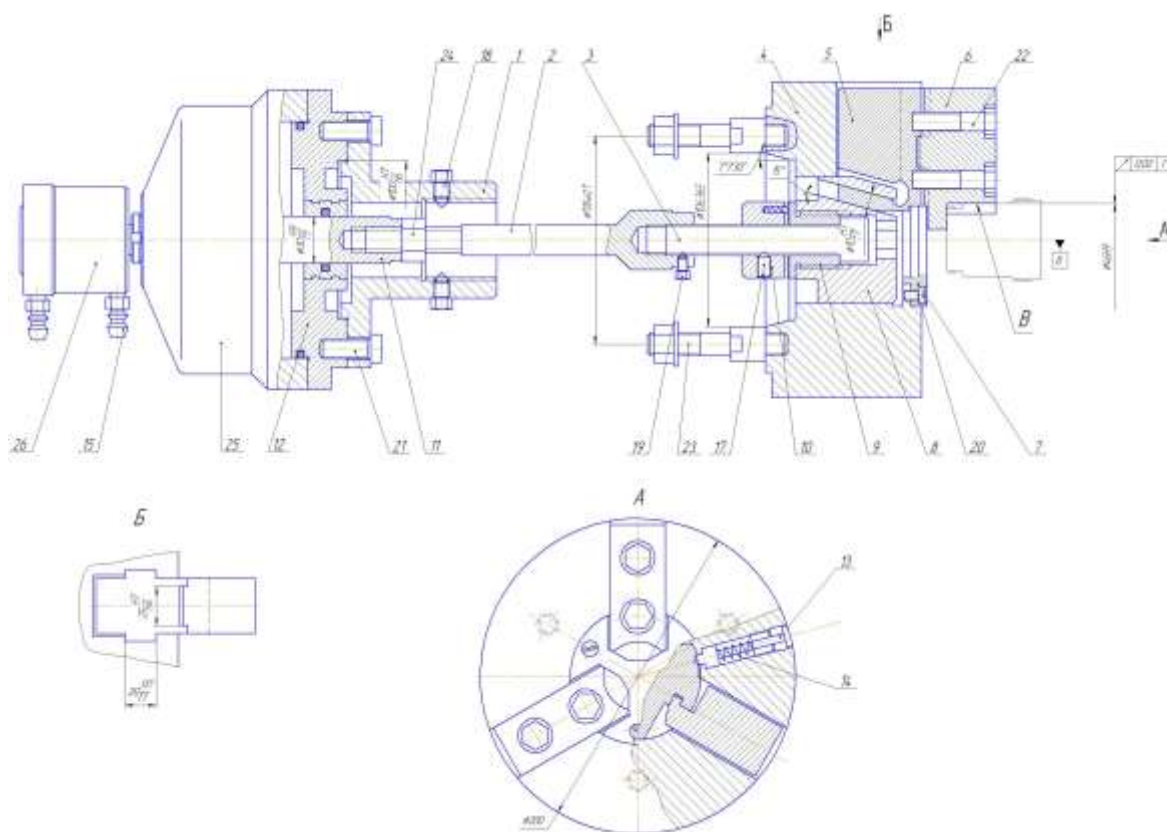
Сборочный чертеж пневматического трехкулачкового патрона
